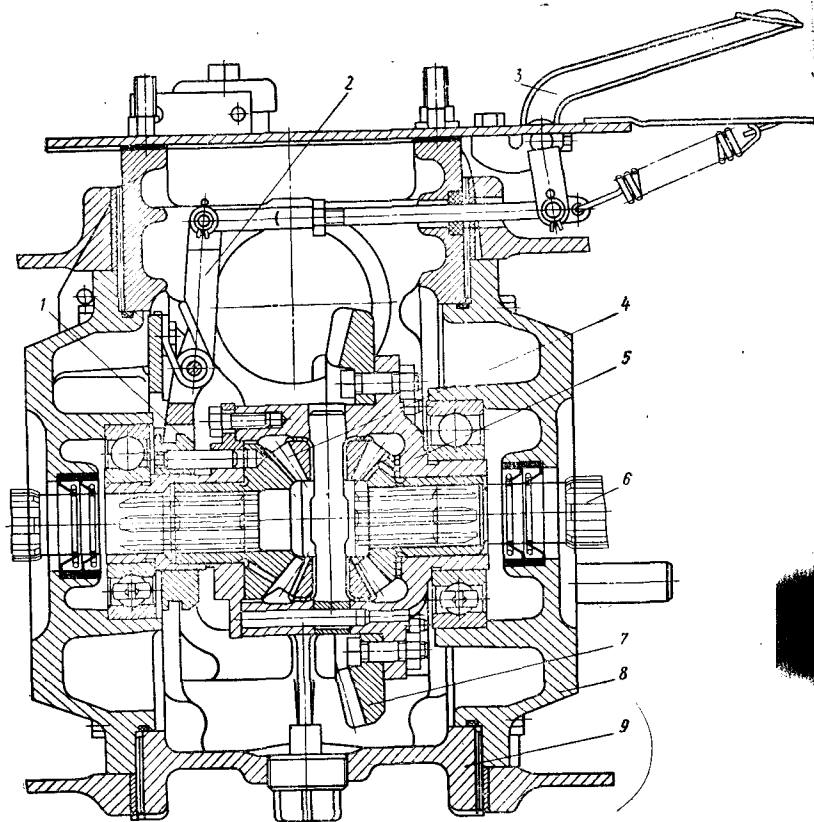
Дифференциал с блокировкой штифтовой муфтой: 1 — штифтовая муфта; 2 — рычаг со спиральной пружиной; 3 — педаль блокировки; 4 — сателлит; 5 — корпус дифференциала; 6 — полуось; 7 — ведомая коническая шестерня центральной передачи; 8 — стакан подшипника; 9 — корпус заднего моста
